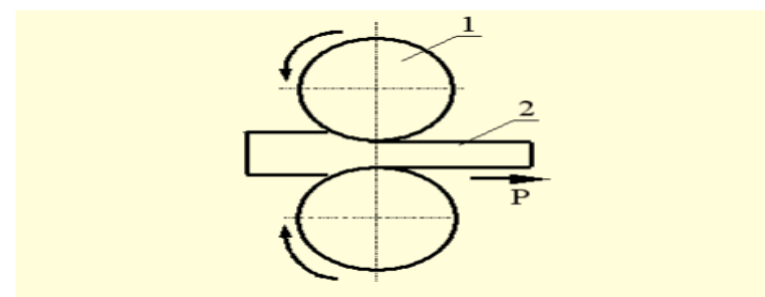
Схема прокатки: 1 – валок; 2 – заготовка
